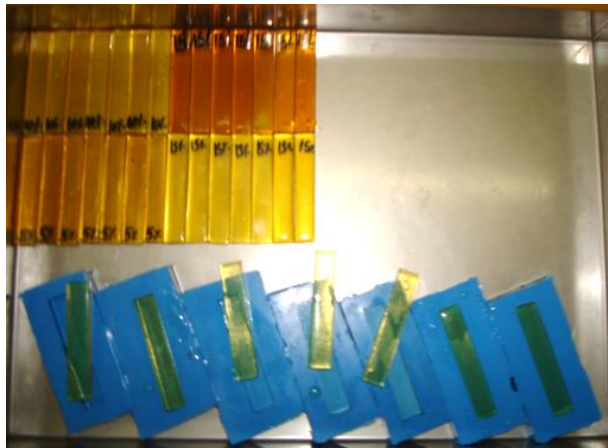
Moldes e corpos de prova para os testes de resistência ao impacto.
